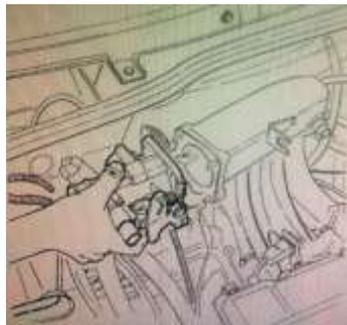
Desmontaje del Cuerpo de Aceleración
